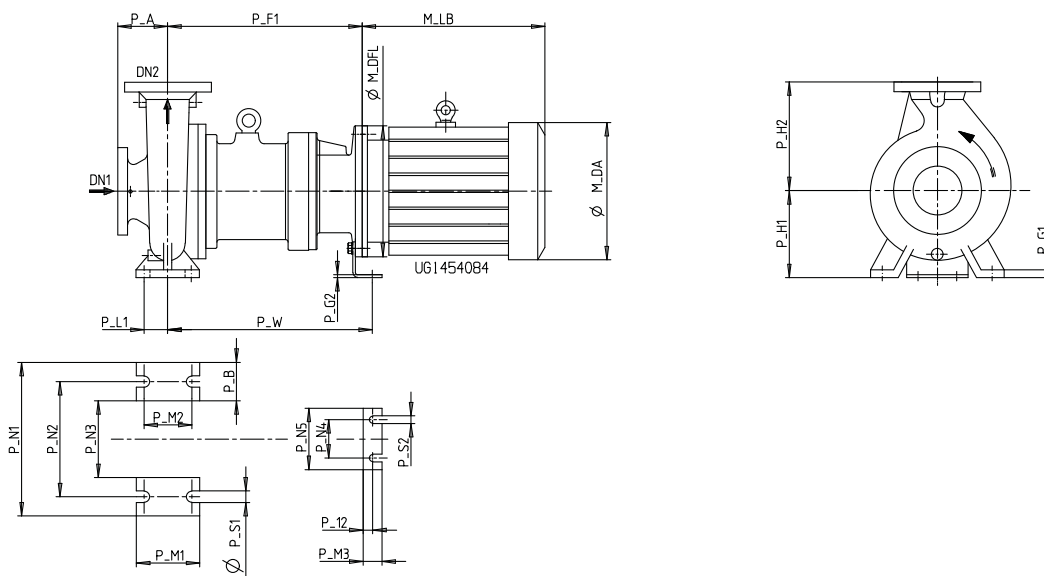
Abmessungen Aufstellung mit Stützfuß
